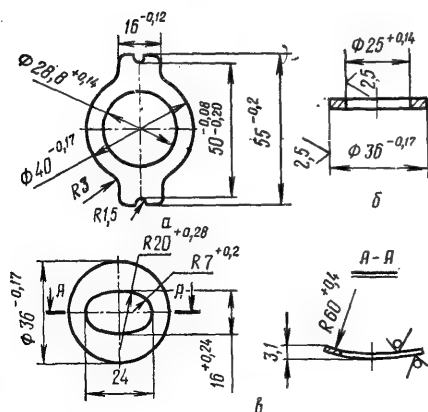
Пластины и пружины клапанов крупных компрессоров:
